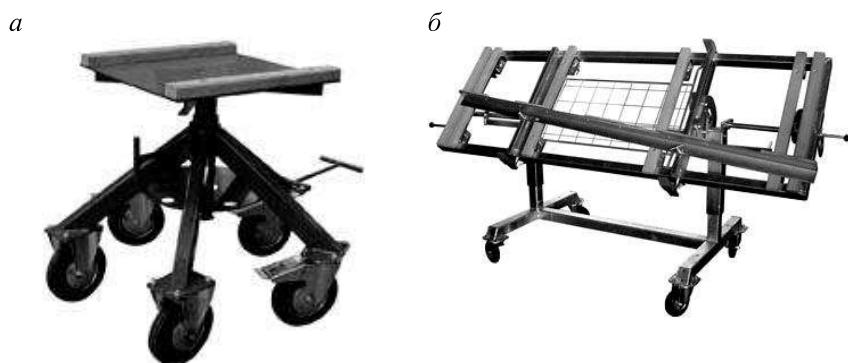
Рухомі поворотні столи для обробки каменю [2]
